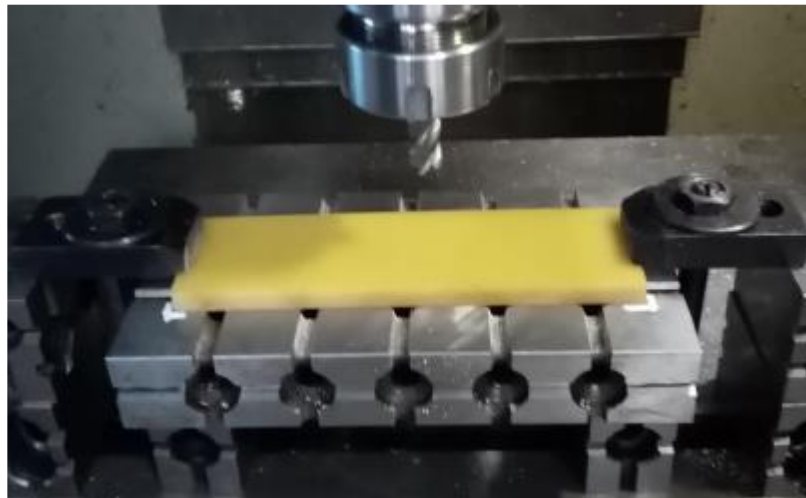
Зона обробки при кінцевому фрезеруванні без притискної пластини
